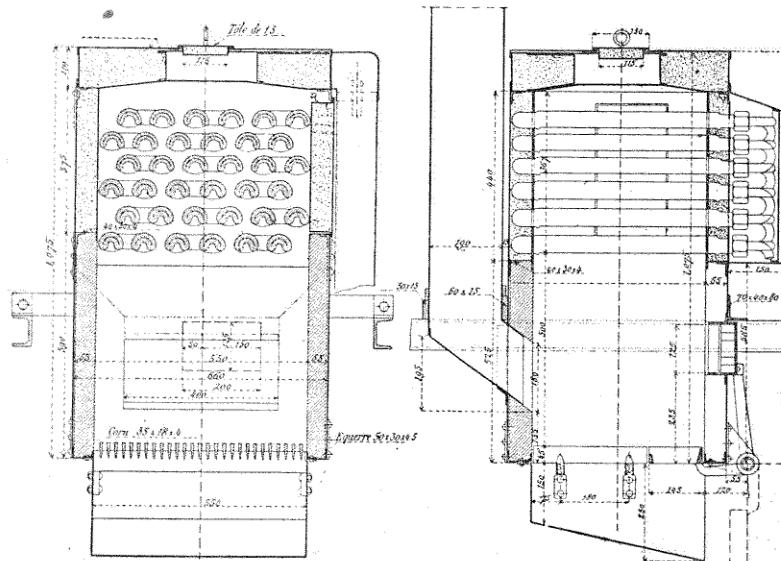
Coupe transversale d'une chaudière Serpollet de 3 m<sup>3</sup> (Echelle de 1/20).
